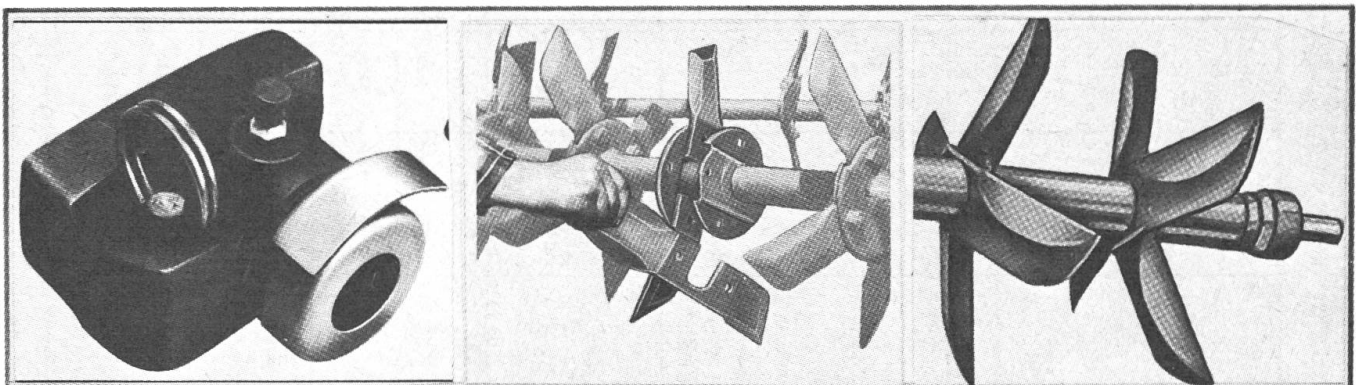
Links: mittels Bolzen lässt sich der Schnittwinkel von Spatenwellen schnell verstellen. Mitte: die Spaten werden kreuzweise mit Schrauben an einem Flansch befestigt oder an einer Vierkantwelle (rechts) eingeschoben.
